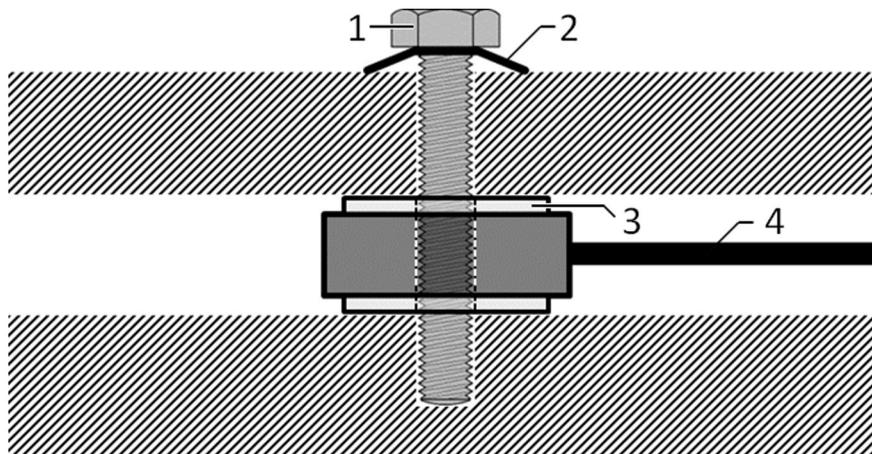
Befestigung des Aktors mit einer Schraube mit Tellerfeder
